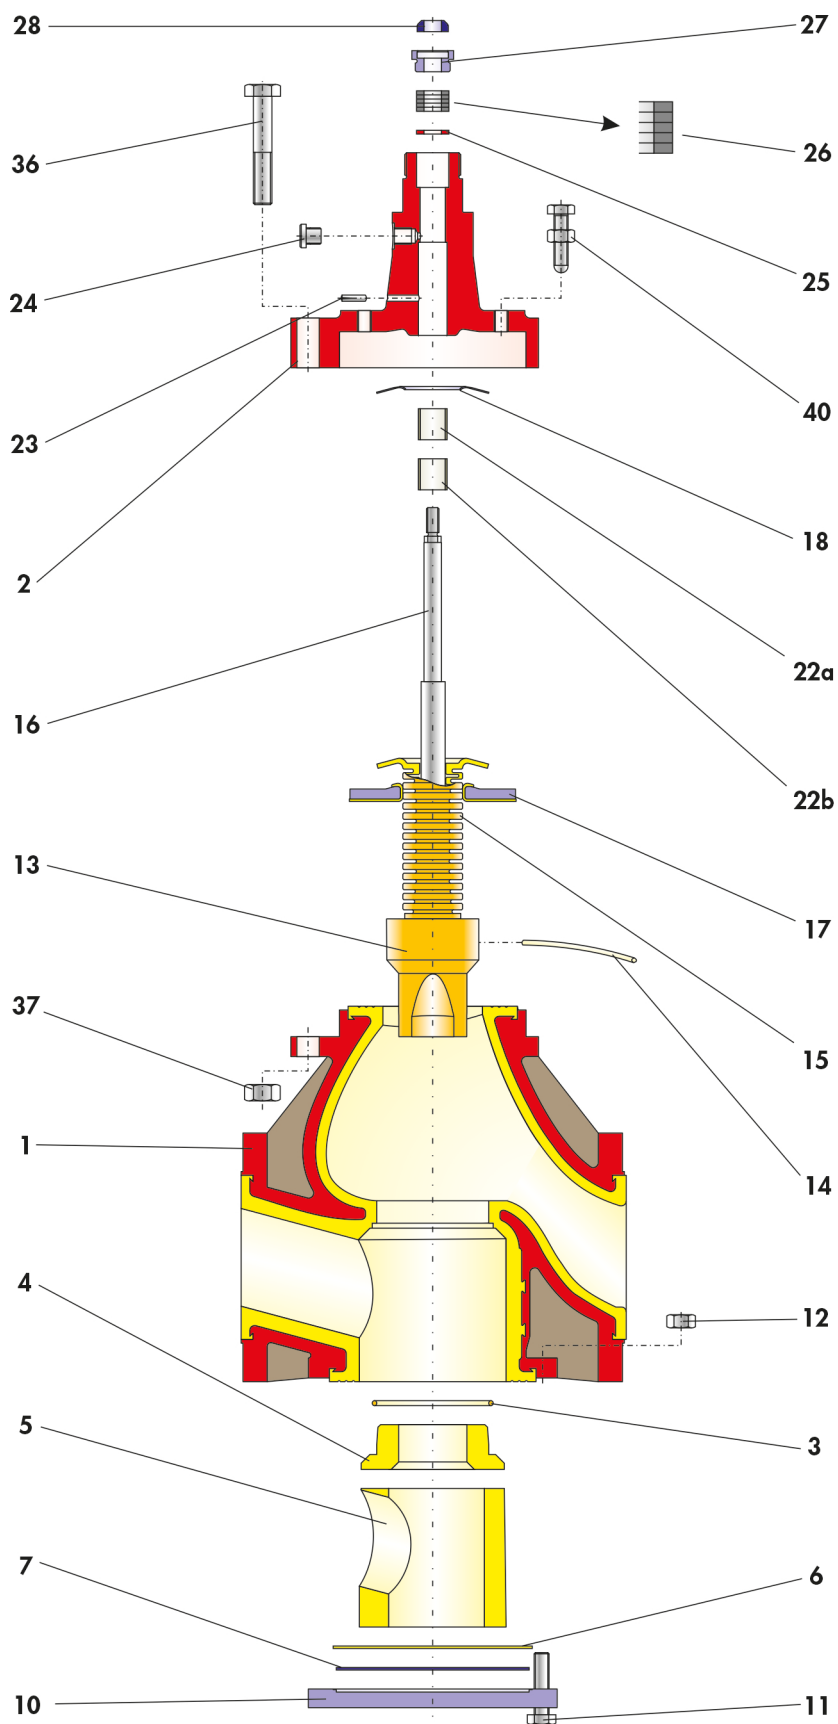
Vue éclatée de la vanne ANSI, NPS4 à 6
